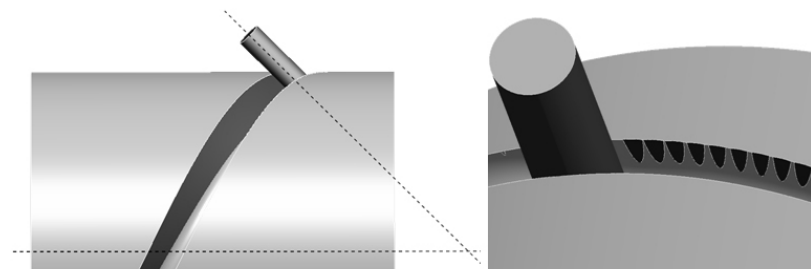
Wendelverteiler mit schrägem Werkzeugeingriff
